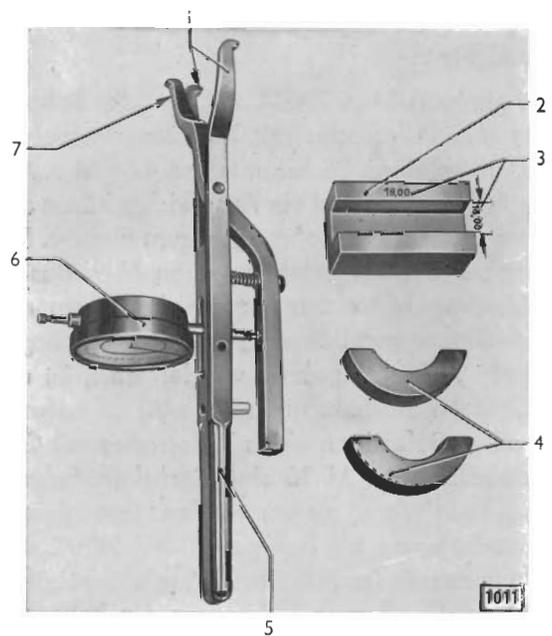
Mehrteiliges Zahnflankenspiel-Einstellwerkzeug S-1202
